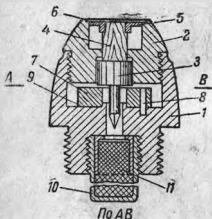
Германский головной ударный взрыватель AZ38: 1 — корпус; 2 — головная втулка; 3 — ударник мгновенного действия с жалом; 4 — ударный стержень; 5 — колпачок; 6 — мембрана; 7 — центробежные плашки; 8 — оси плашек; 9 — кольцевая пружина; 10 — запальный стакан; 11 — капсюль-детонатор
